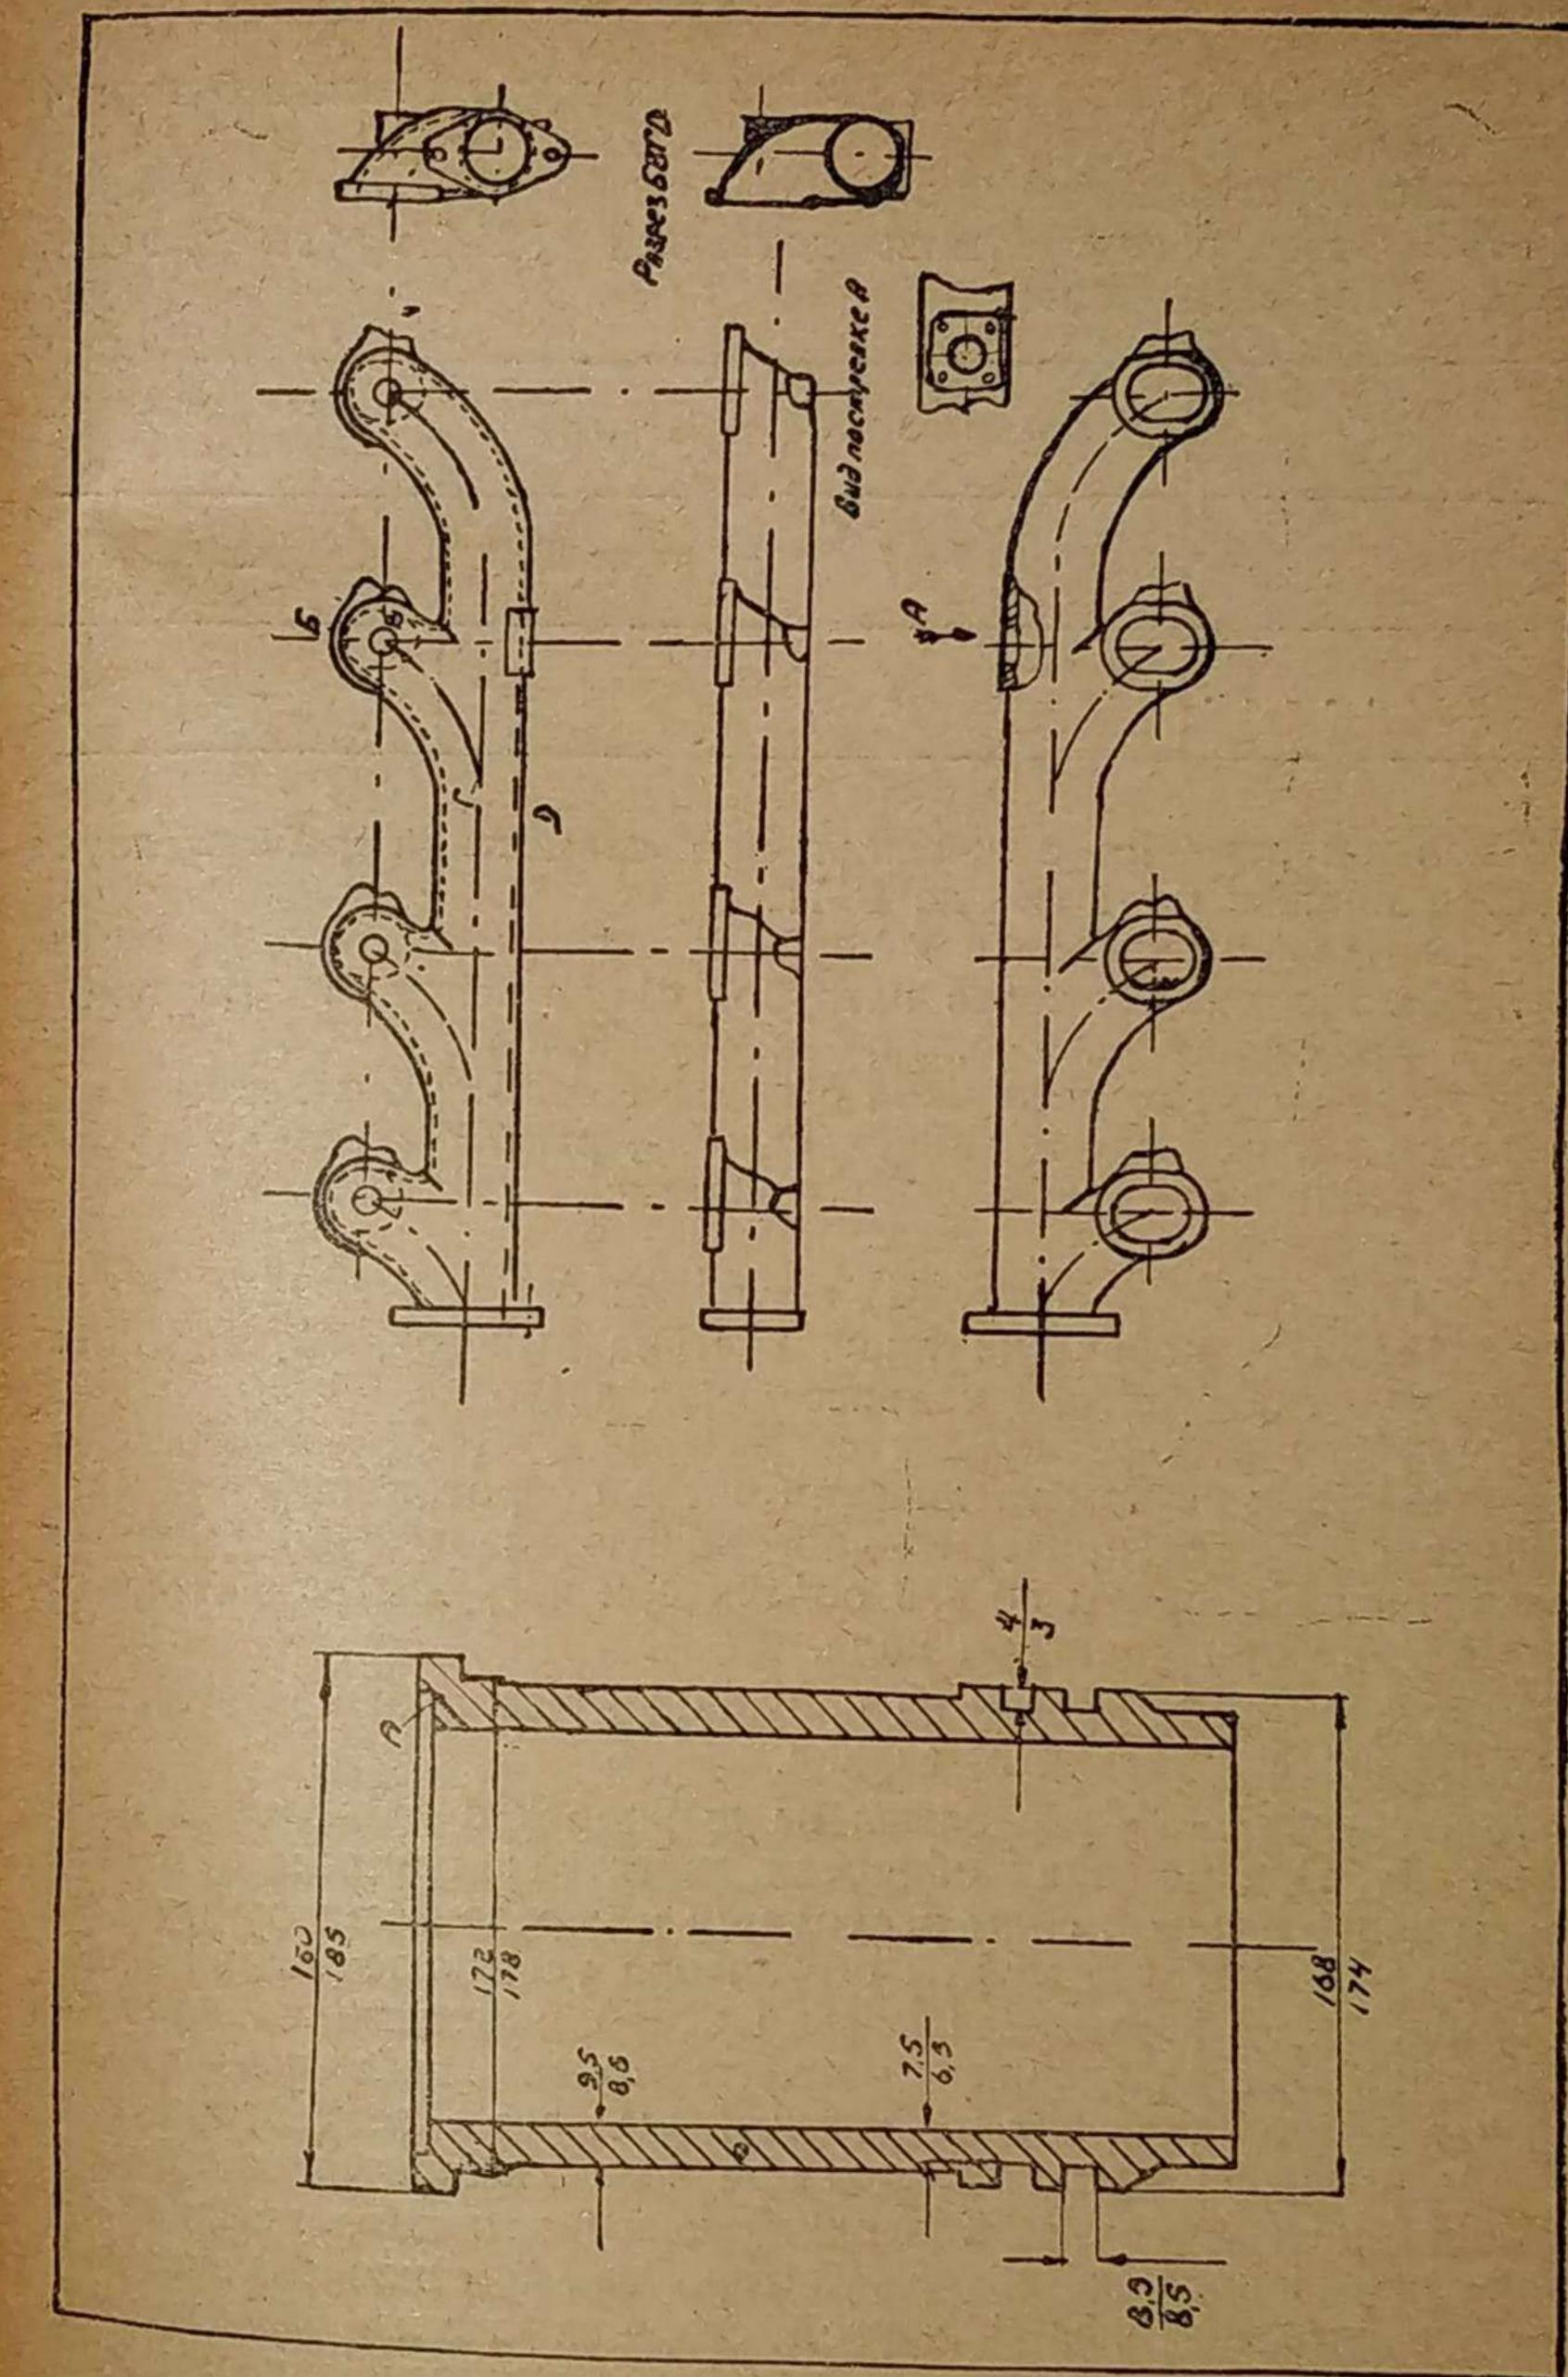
Вставная гильза цилиндра и всасывающая труба двигателя «МГ-17».
